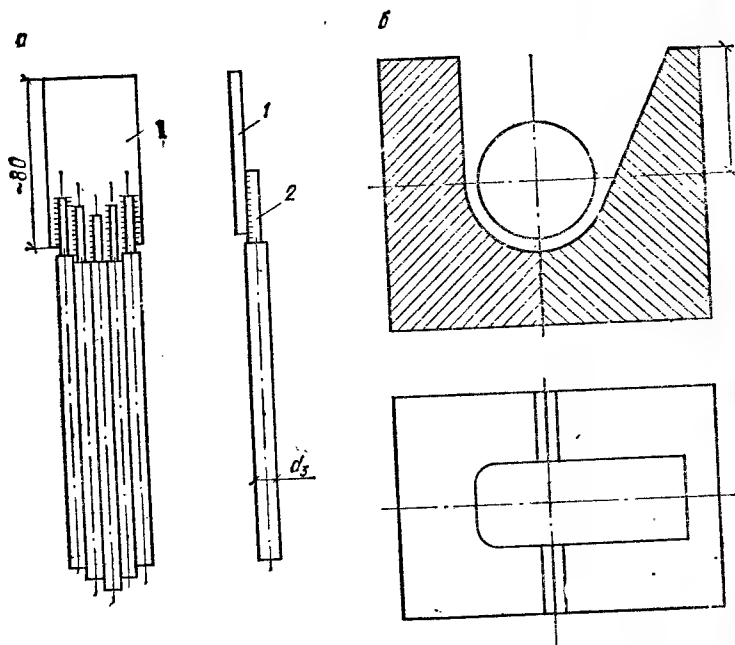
Гребенка электродов (а) и конструкция медных форм для дуговой многоэлектродной ванной сварки труднодоступных соединений однопорядковых горизонтальных стержней (б)
